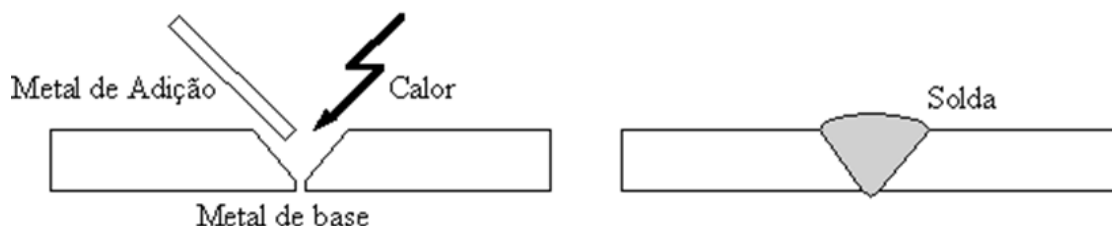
Esquema do procedimento de soldagem, sendo que o cobre foi adicionado intencionalmente entre passes de solda.⁽⁵⁾
